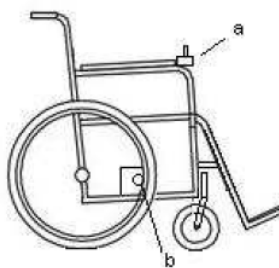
Transmissão por engrenagem no eixo, (a) - *joystick*, (b) - Motor com engrenagem, (c) - Engrenagem acoplada diretamente ao eixo da roda para transmitir o movimento do motor
